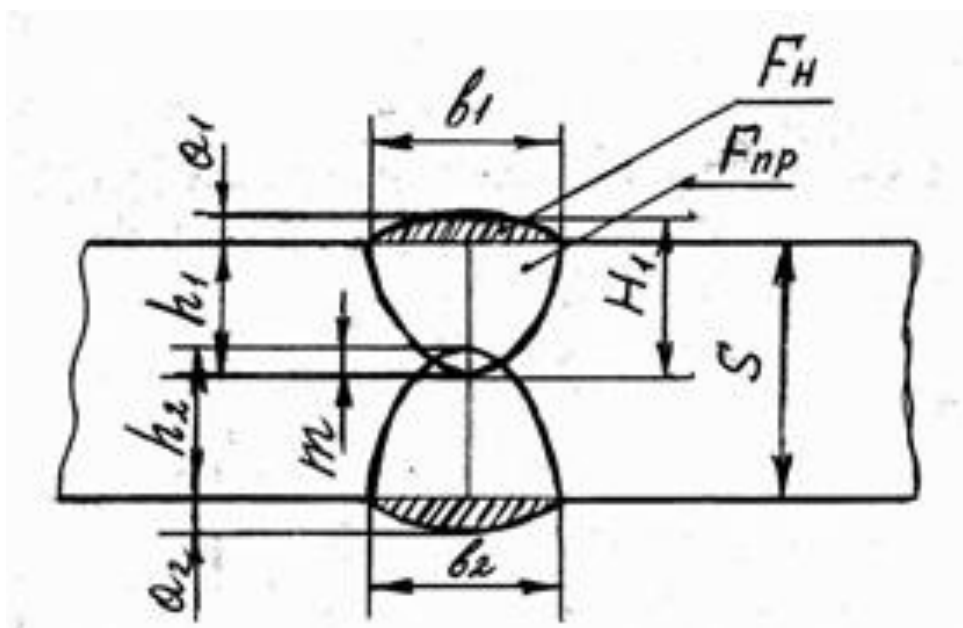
б – Основні геометричні розміри стикового шва при двобічному зварюванні
